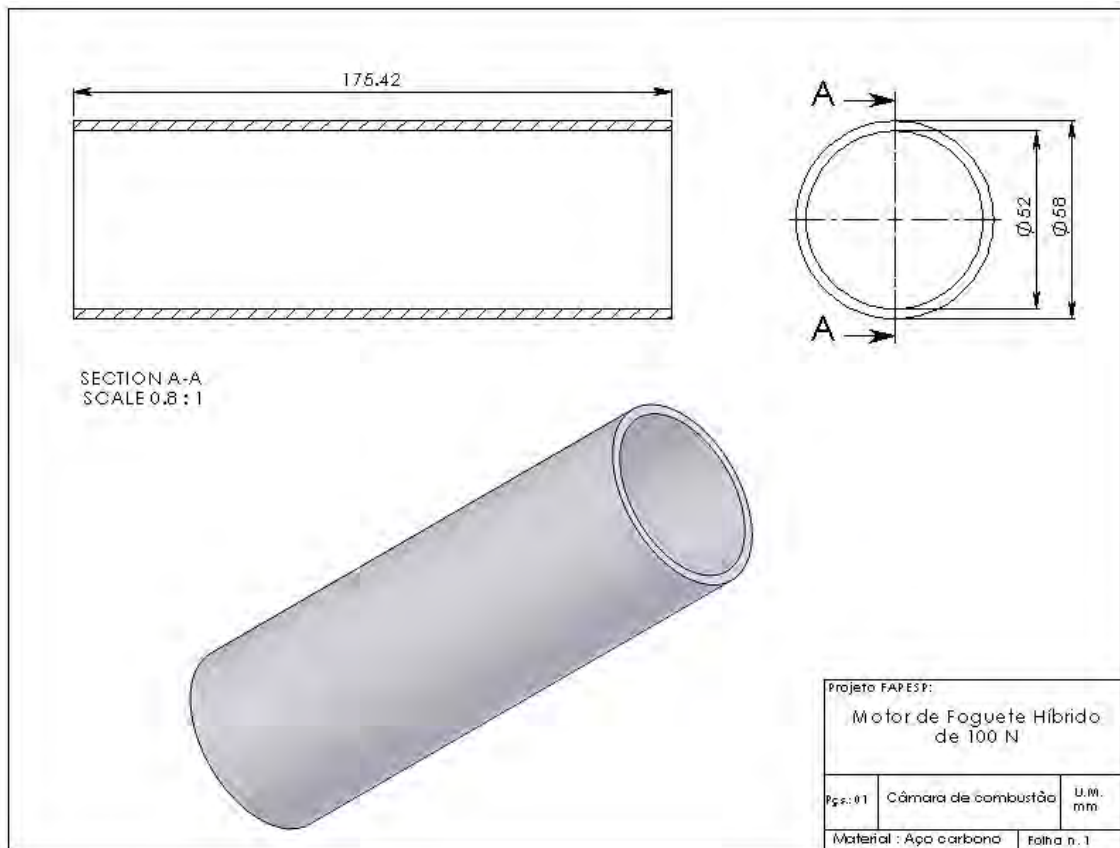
Desmontagem do motor foguete híbrido, cotas da câmara de combustão.
